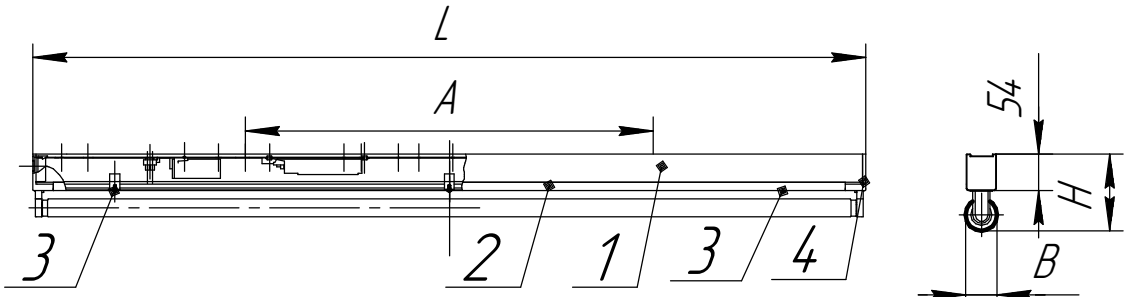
1. Корпус в сборе, 2. Крышка, 3. Винт, 4. Крышка.
